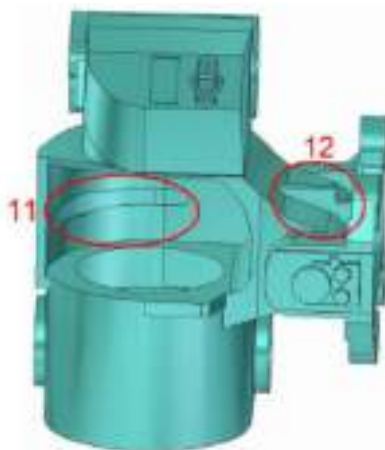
Модифікації корпусу гальма під номерами 11-12.
